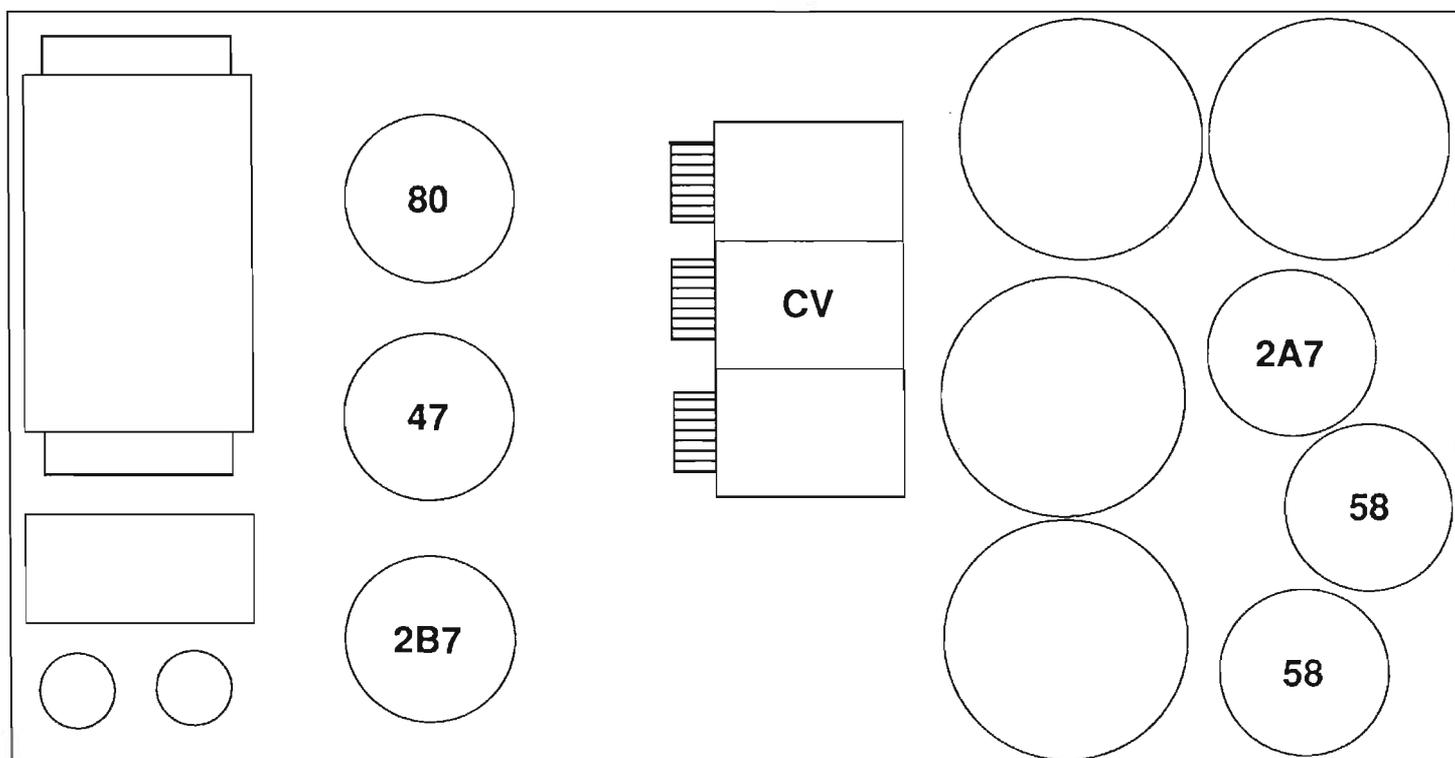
Disposition des éléments sur le chassis — Top view showing the layout of components
